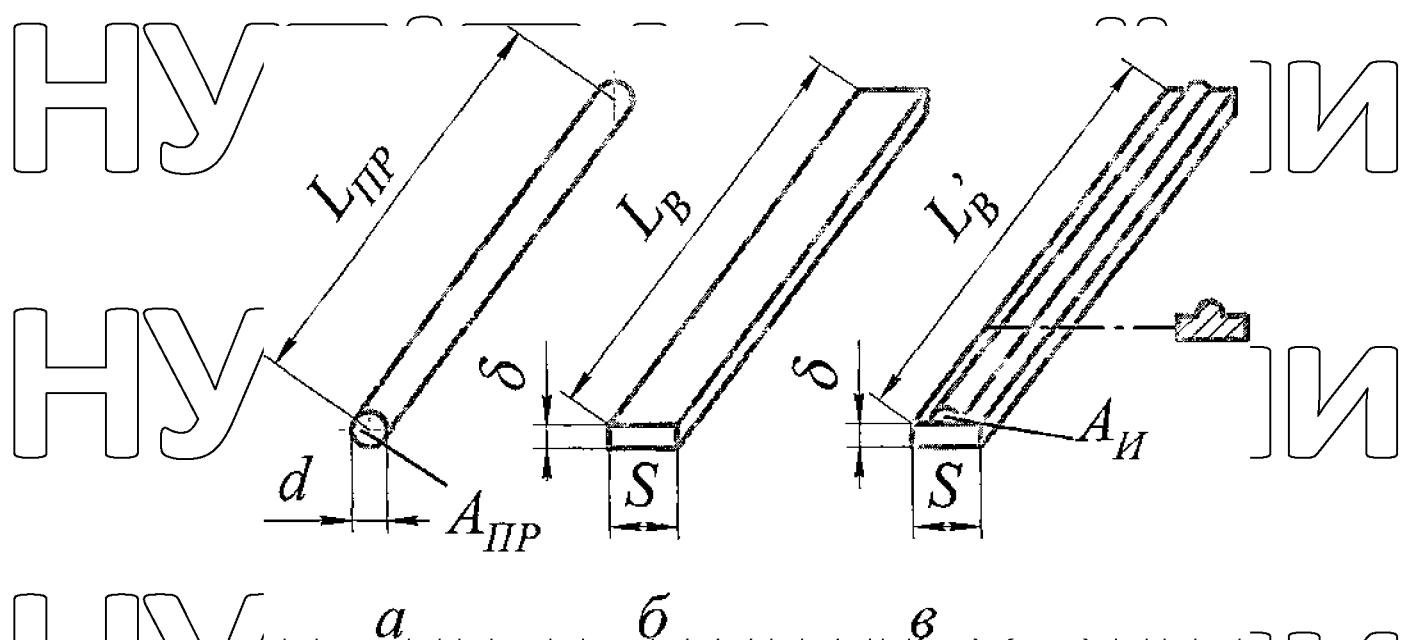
Розгортки валиків металопокриття: а – вихідний присадний дріт; б – валик, наплавлений незношеним ролик-електродом; в – валик, наплавлений зношеним ролик-електродом.
